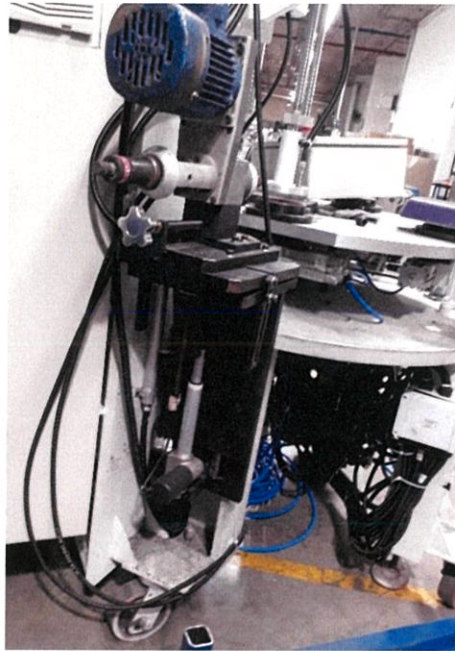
ภาพรวมเครื่องเชื่อมเม็ดสตัด (Stud Welding Machine)
